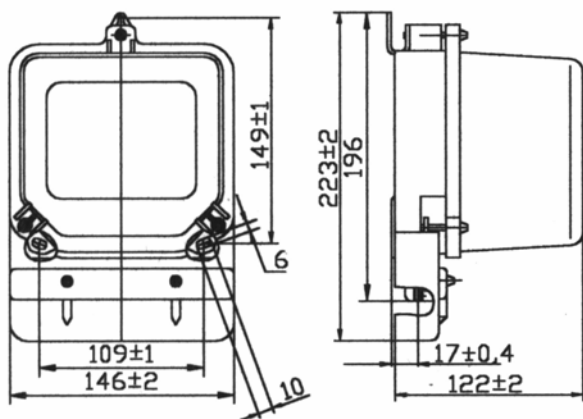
Габаритные и установочные размеры счетчика СО-ЭЭ6705
